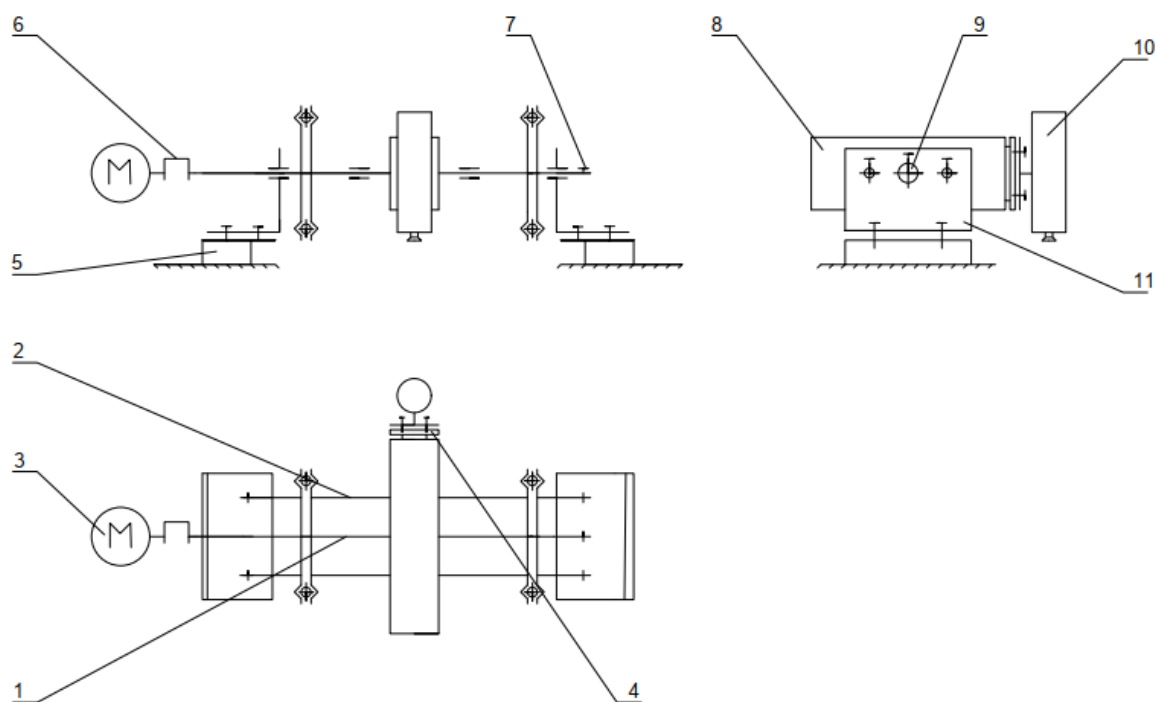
Кинематическая схема портативного станка для плазменной резки
